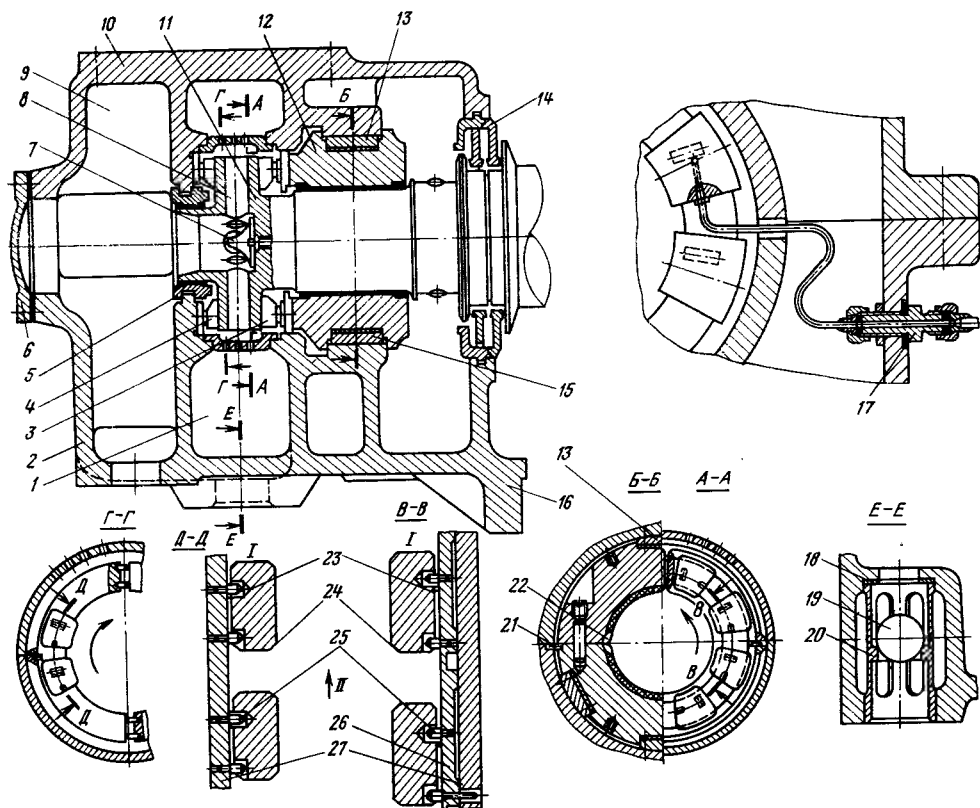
Опорно-упорный подшипник КТЗ:
